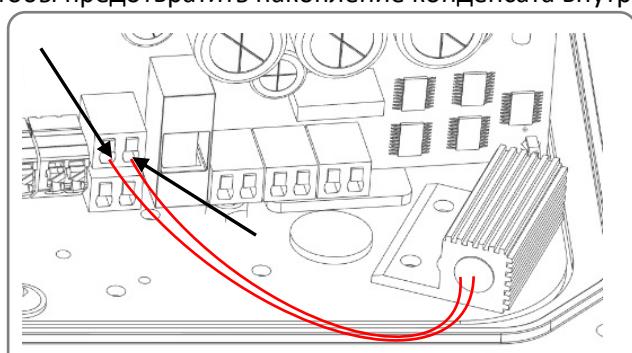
Установка и подключение обогревателя PSQ103 - 203AMS
